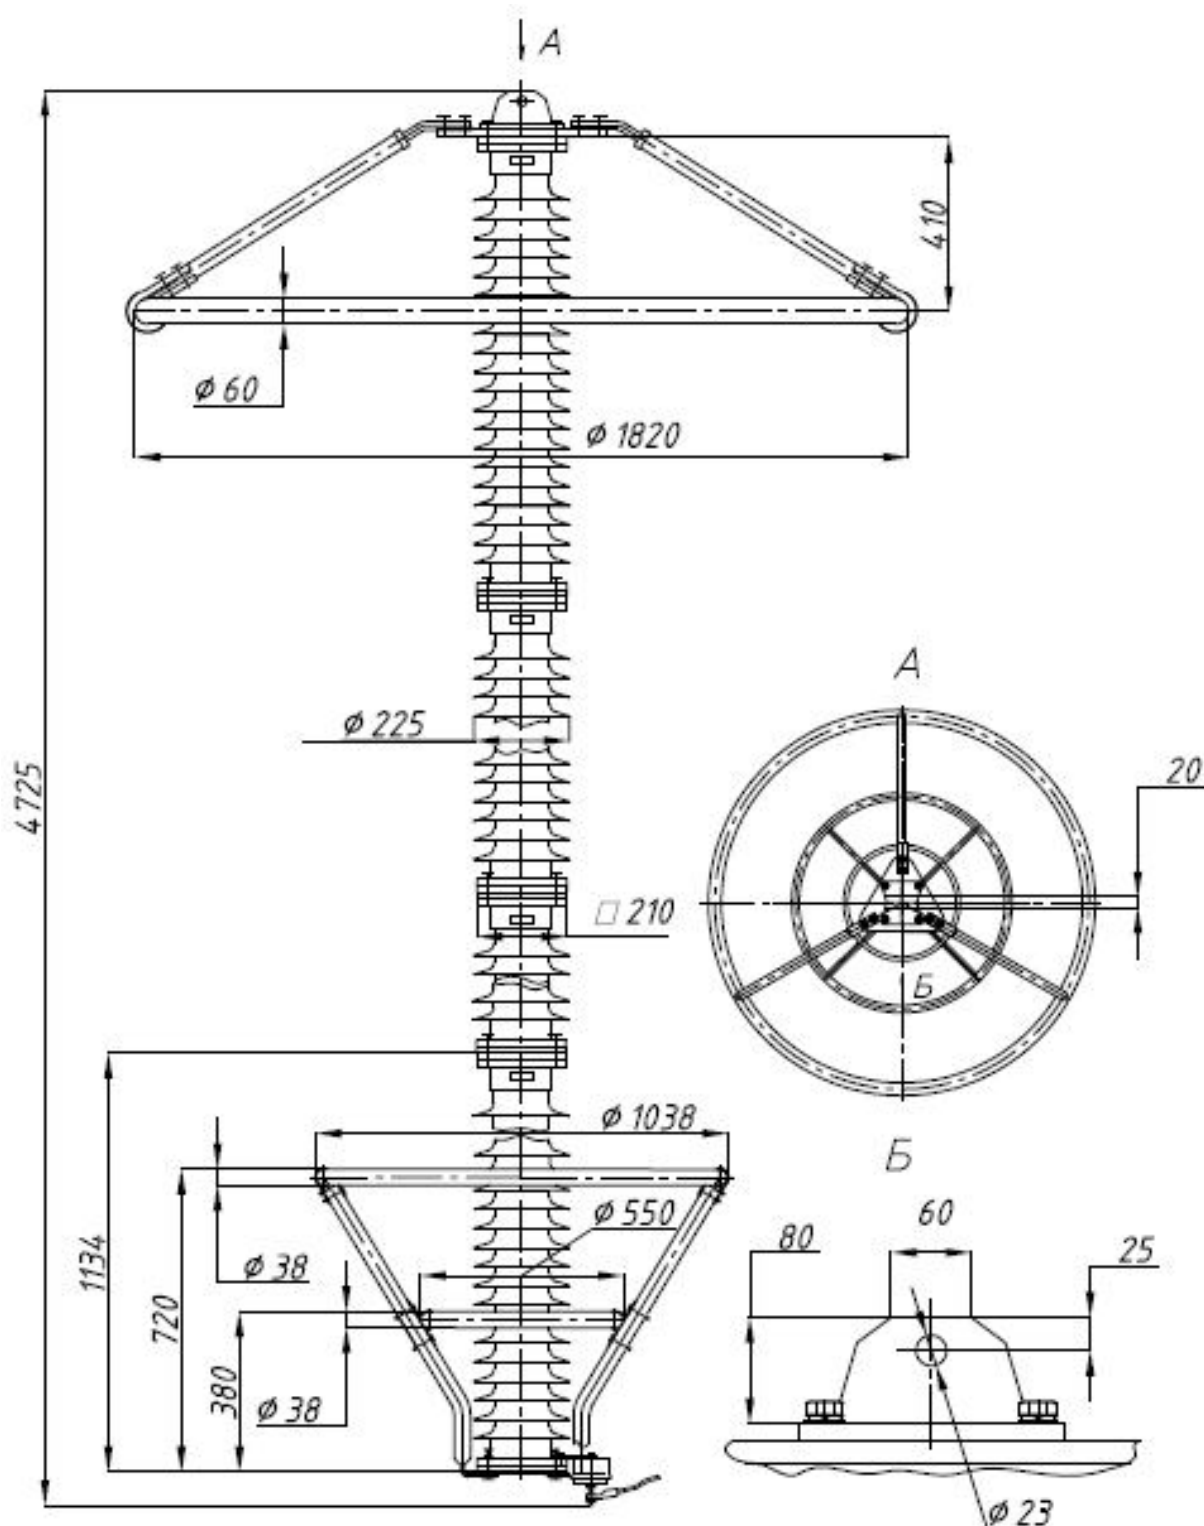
ОПН-Л габаритные, установочные и присоединительные размеры.
